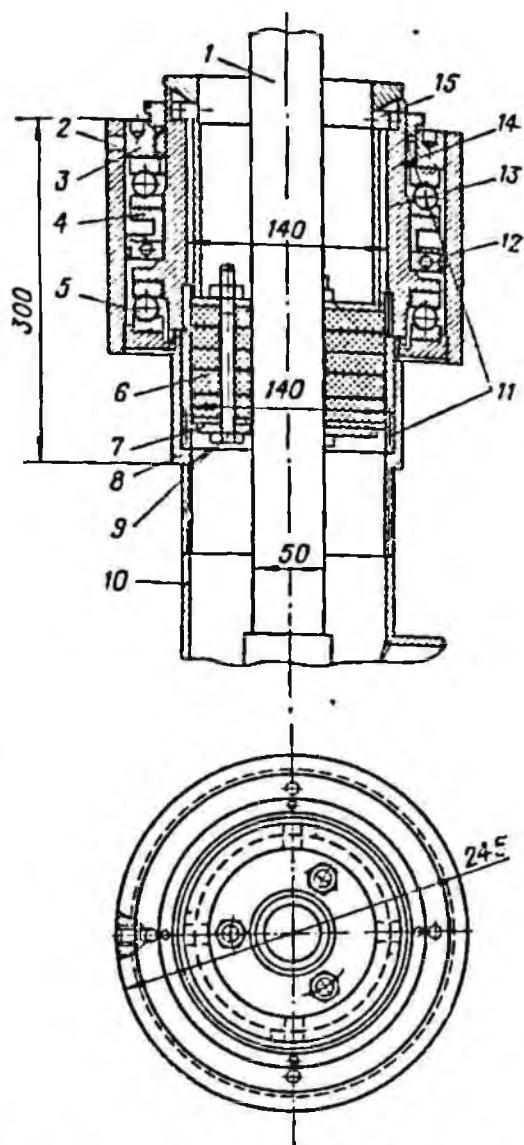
Вращающийся пакер для герметизации устья скважины (Иркутский политехнический институт).
